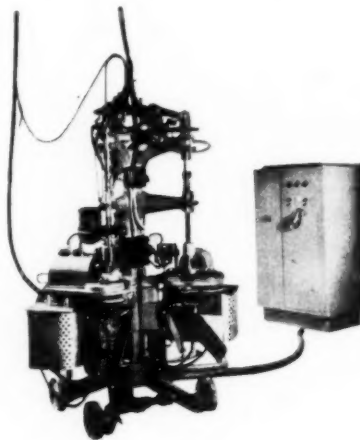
Machine à couper les gobelets par haute fréquence permettant de couper 8 500 gobelets en 2 1/2 h; la durée de coupe par gobelet est de 8 à 10 s (Union technique des verreries).
